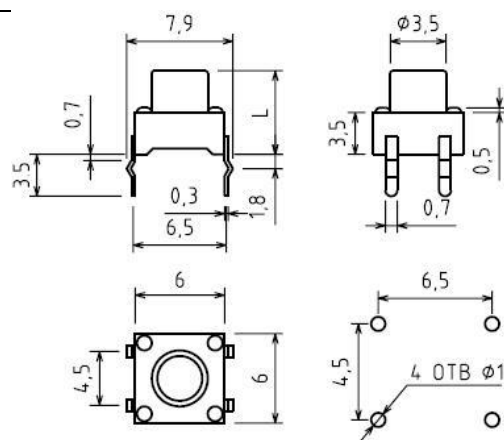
Габаритні розміри кнопки KLS7-TS6601-13.0-180
